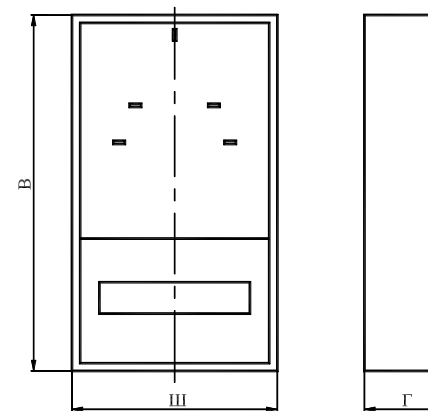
Габаритные размеры корпусов металлических ЩРУЭН
